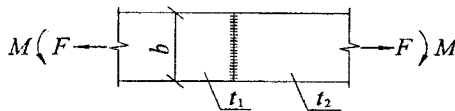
Розрахункова схема стикового зварного з'єднання
